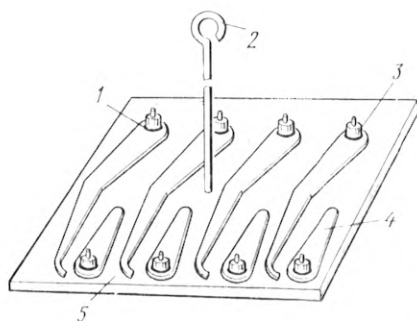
Приспособление для пайки деталей, закрепленных на плите:
